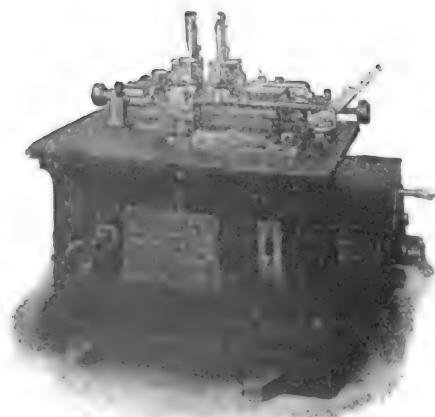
Machine à souder type 1-A, pour la soudure des petits fils de cuivre.
